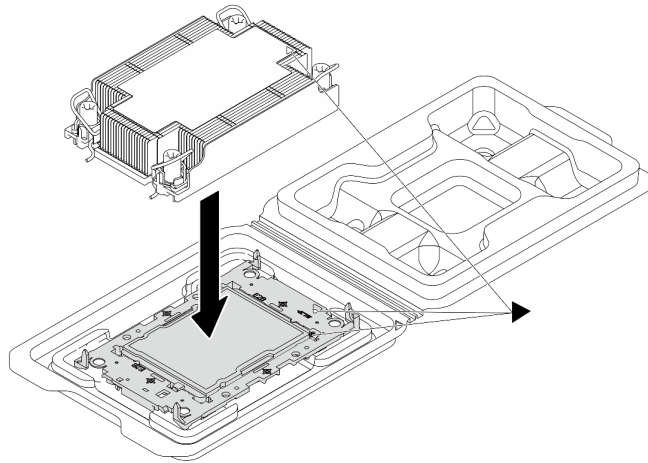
Assemblage du module de processeur-dissipateur thermique avec le processeur dans le plateau d'expédition
